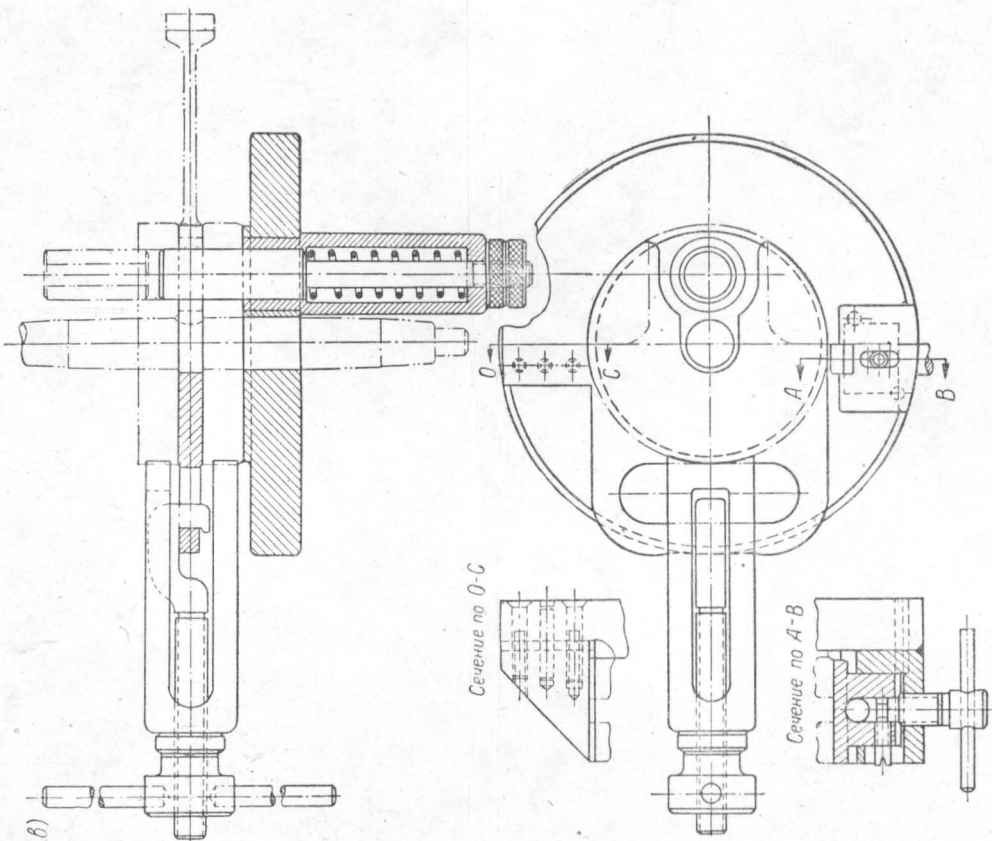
Приспособление для запрессовки и распрессовки кривошипно-шатунного механизма:
